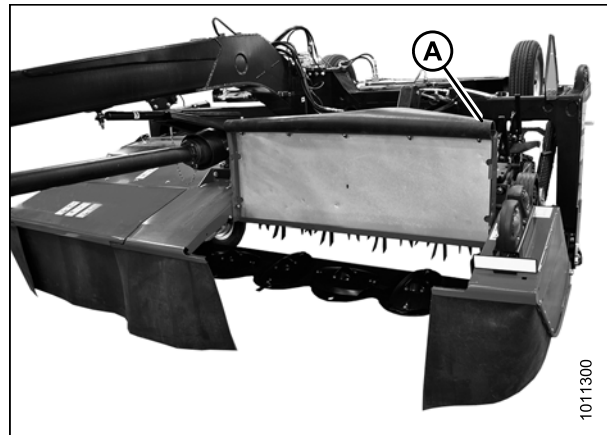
Porte de la barre de coupe du côté gauche ouverte
